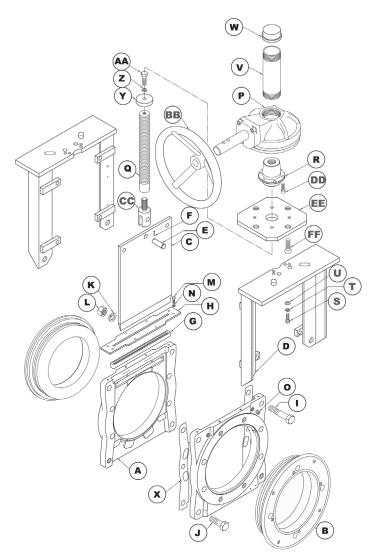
VISTA EXPLODIDA KGD-MH
